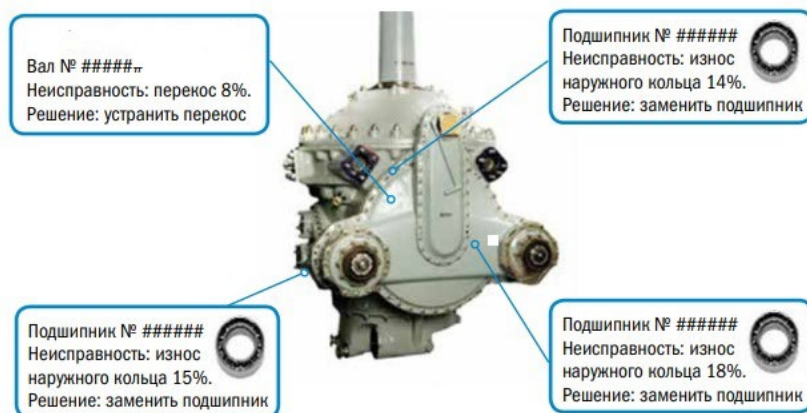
Схема стану деталей головного редуктора вертольота [24]
